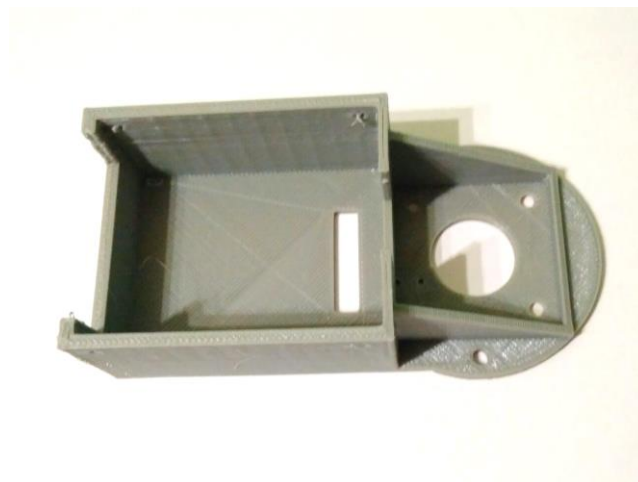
Приклад готової деталі корпусу, що роздрукована за допомогою 3D принтеру
